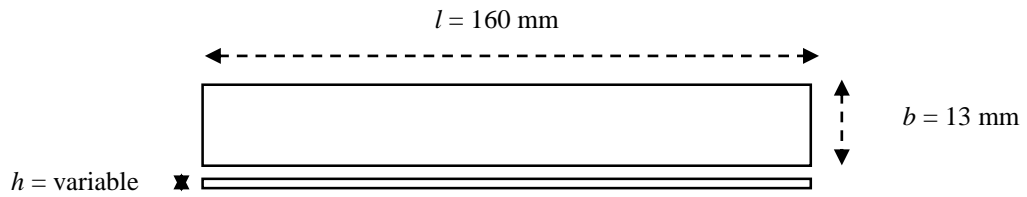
Dimensiones de probeta para ensayo a Flexión
